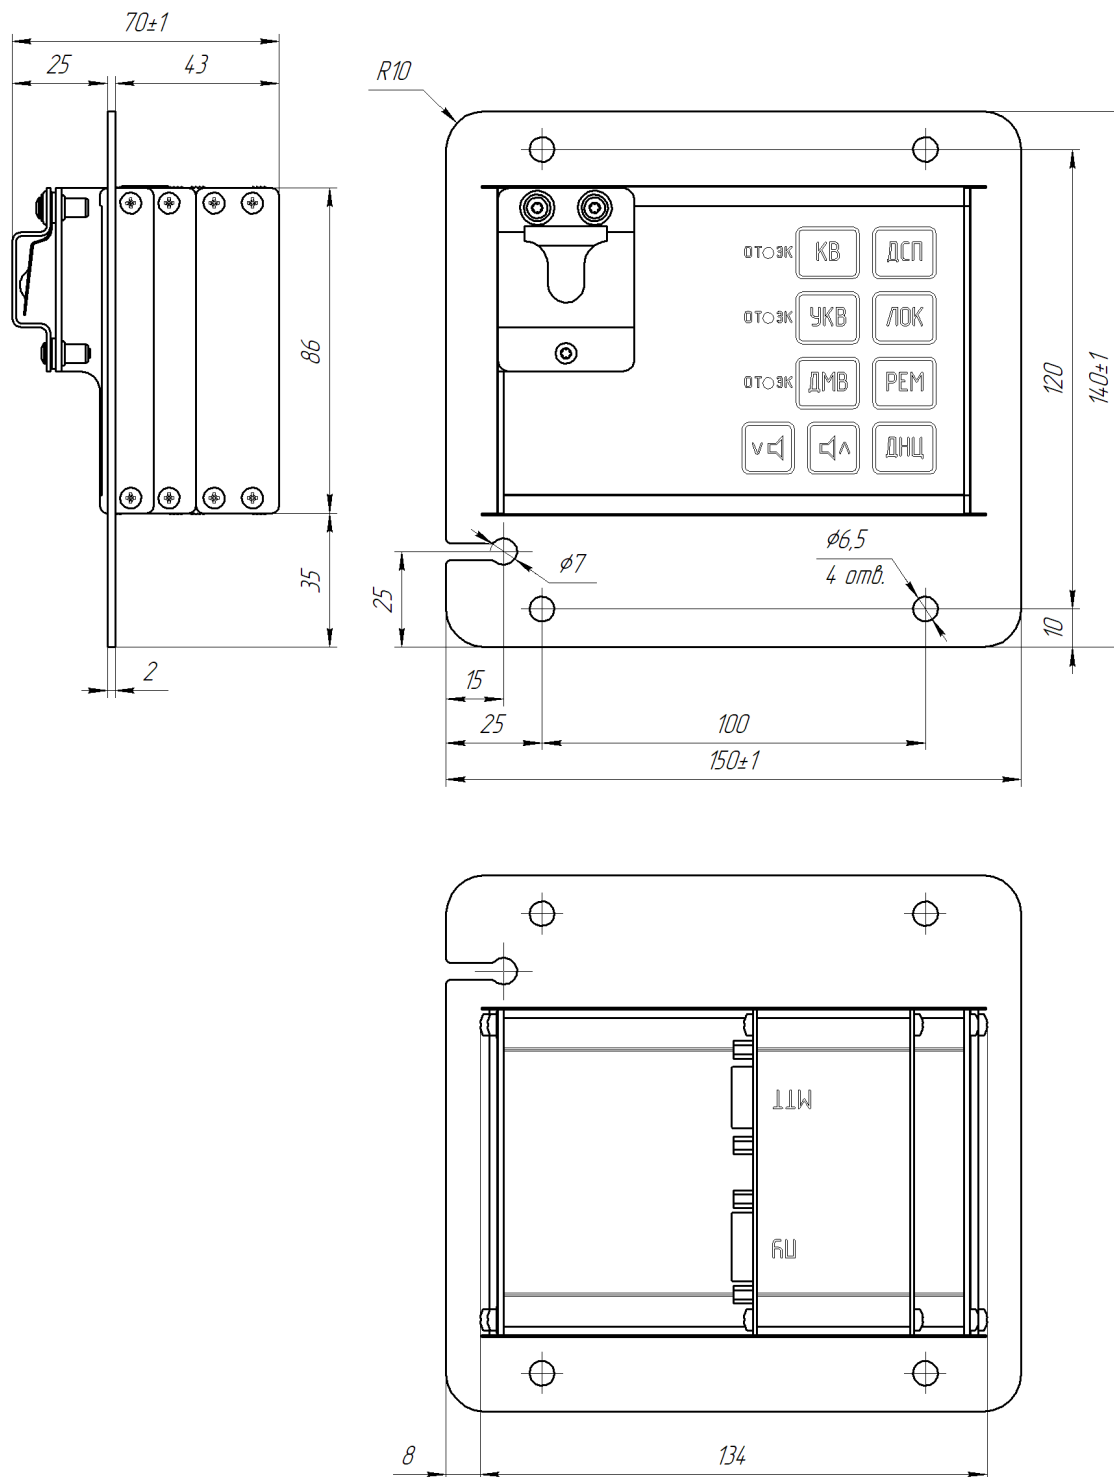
Габаритные и установочные размеры ПД-В
